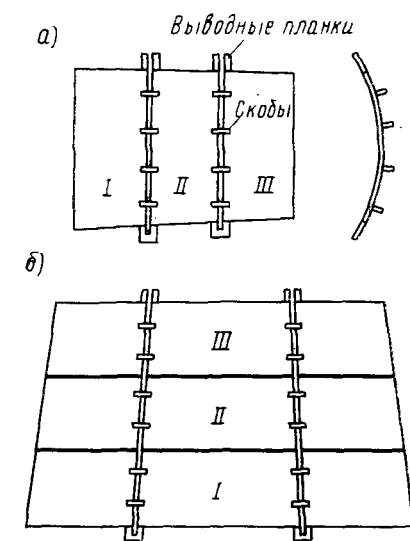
Схемы сборки под электрошлаковую сварку:
